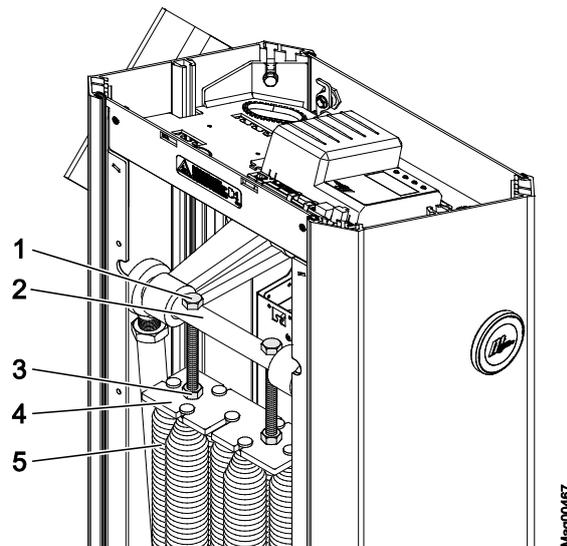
Ausgleichsfedern Access XL2 und Access XXL einstellen
